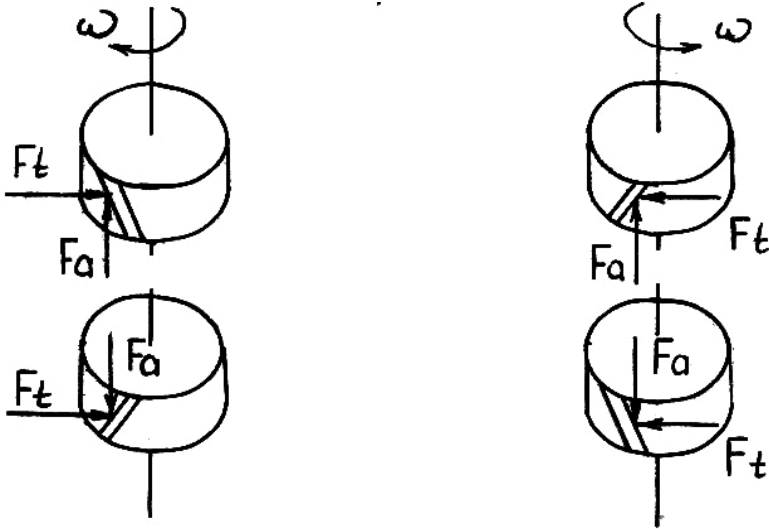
Направления сил на ведущем колесе цилиндрической косозубой передачи
